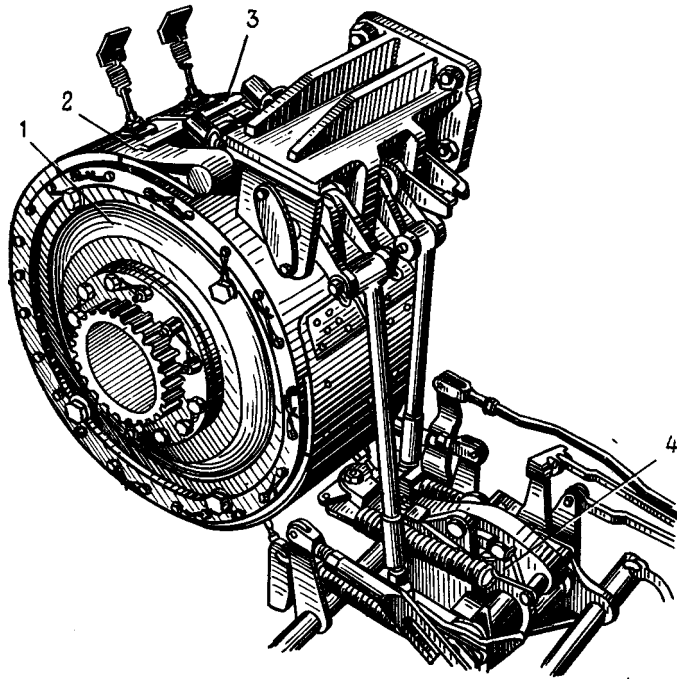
Механизм поворота и остановочный тормоз (общий вид):
